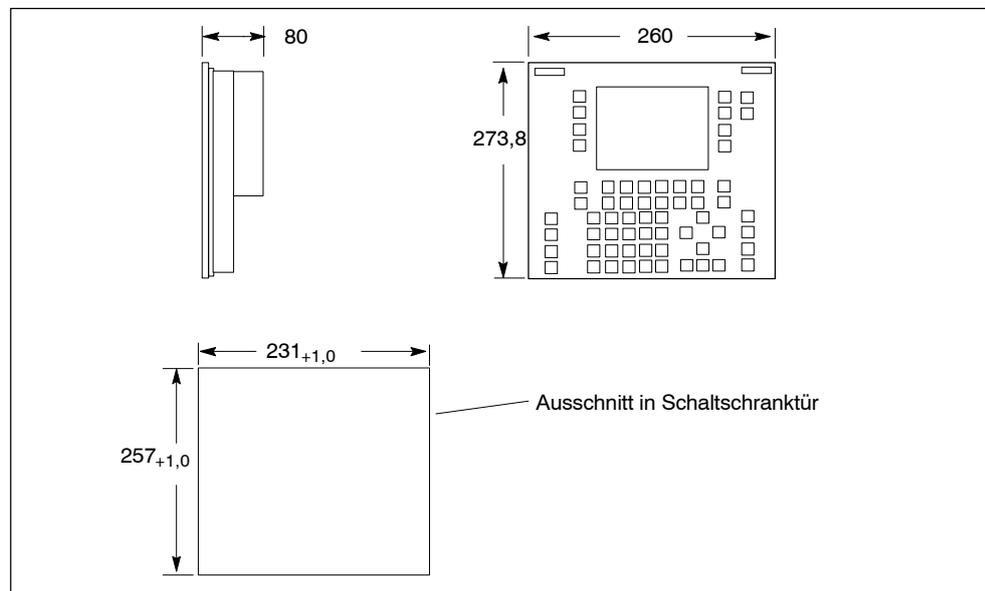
Maßbilder für das C7-635 Key (Maße in Millimeter)
